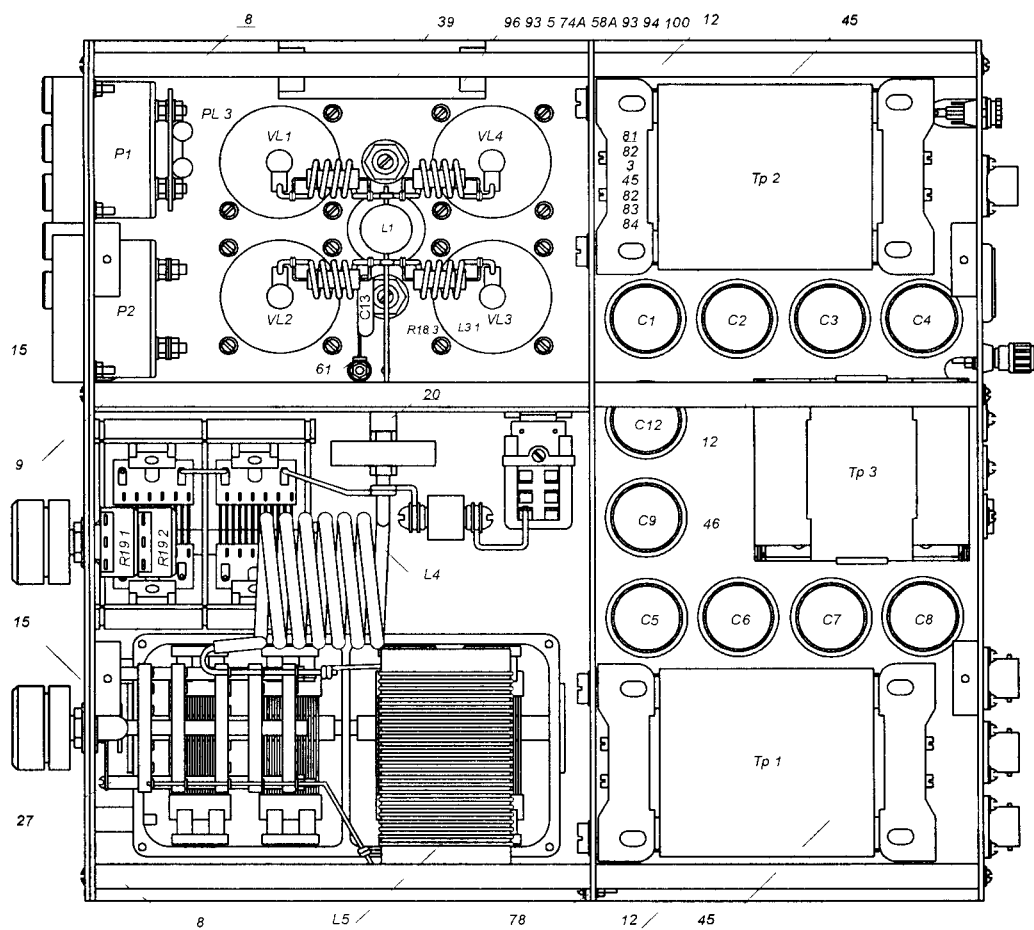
Е Сборочный чертеж усилителя DVA-300E Вид сверху со снятой верхней крышкой
